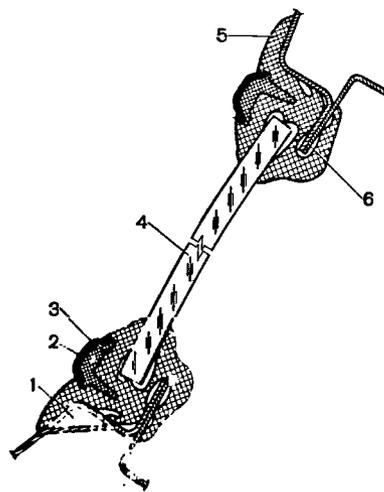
Ветровое стекло с уплотнителем в сборе: 1 - выштамповка для стока воды; 2 - облицовка окантовки уплотнителя; 3 - окантовка уплотнителя; 4 - стекло; 5 - уплотнитель; 6 - фланец проема ветрового окна
